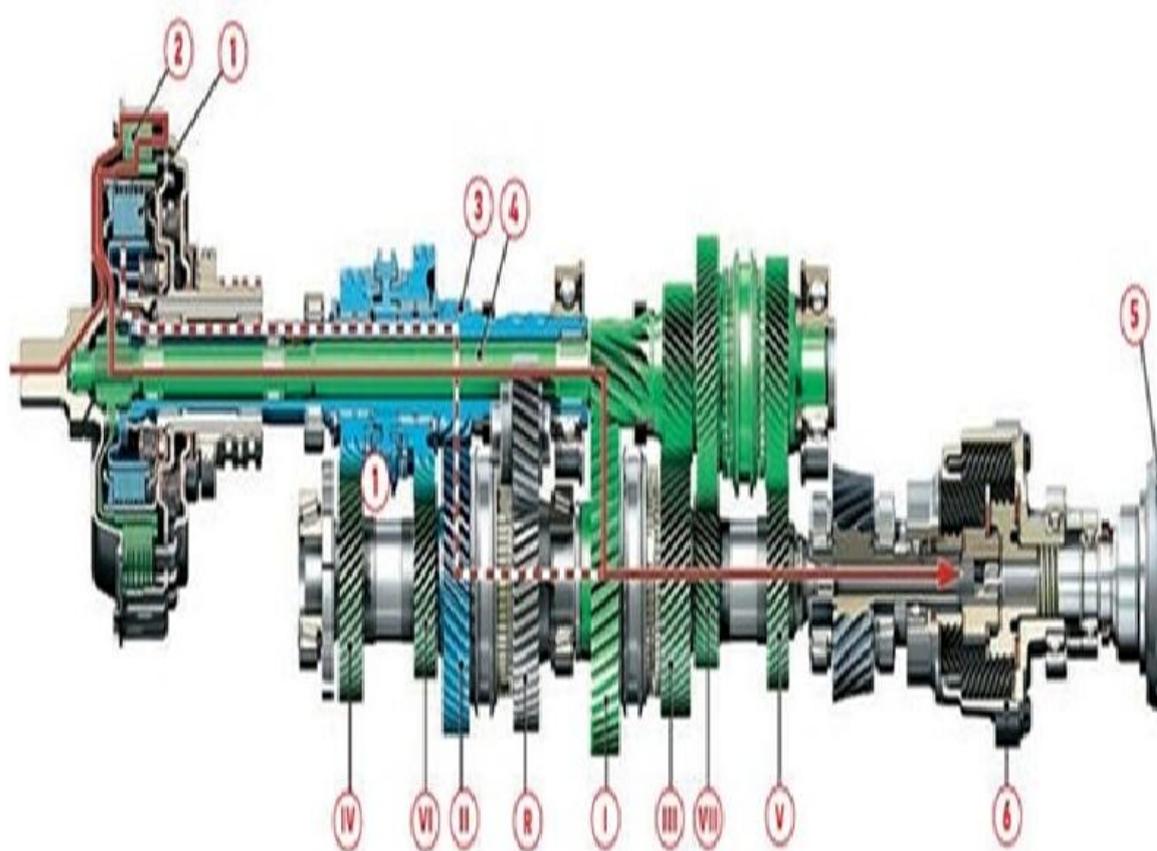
Схема трехвальной коробки передач с двойным сцеплением: 1 – сцепление №1; 2 – сцепление № 2; 3 – первичный вал четных передач; 4 – первичный вал нечетных передач; 5 – привод на колеса; 6 – дифференциал; I-VII – передачи для движения вперед; R – задняя передача
